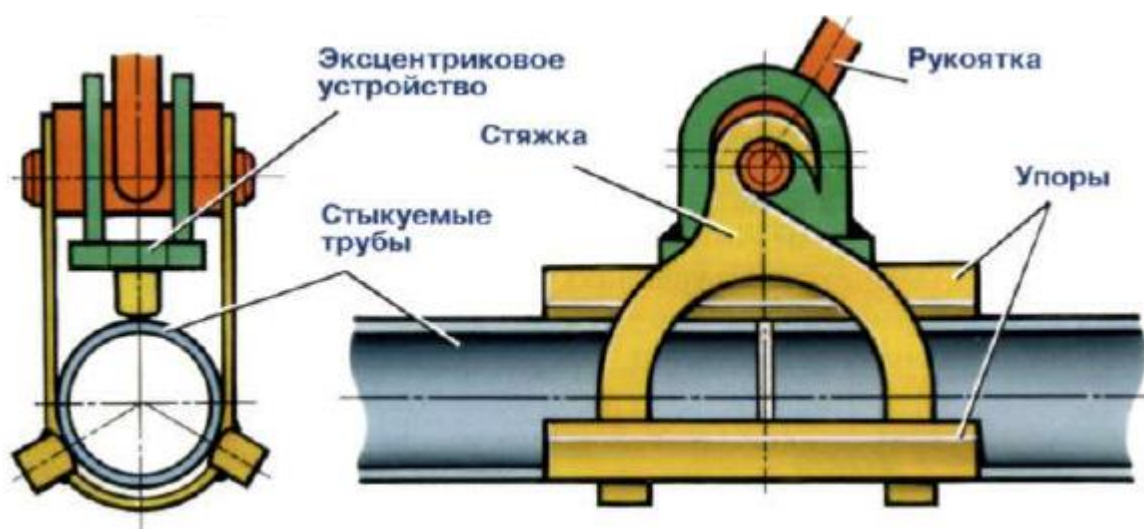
Сборка труб под сварку с использованием наружного центратора
